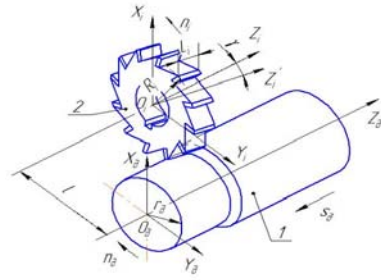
Схема фрезерування циліндричного вала зі схрещеними осями інструмента та деталі
